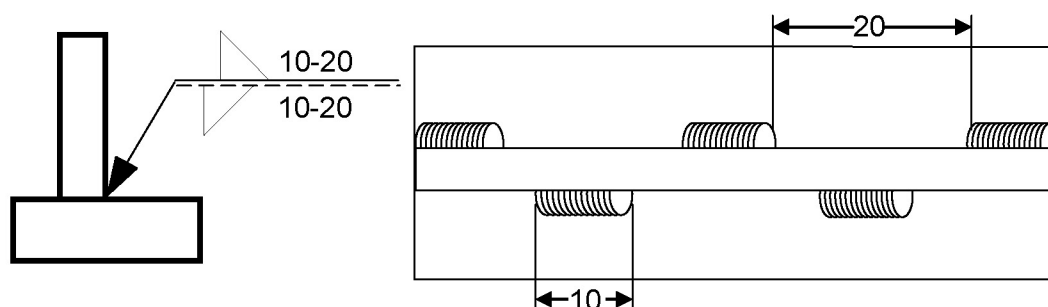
Soldaduras en ángulo con cordones discontinuos alternados
